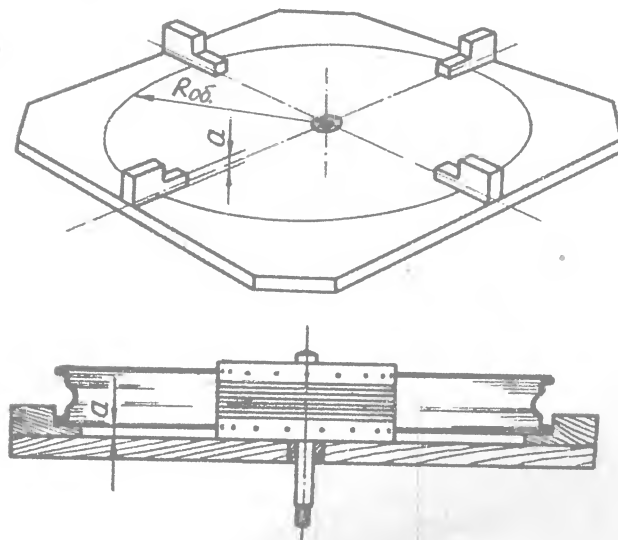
Приспособление для сборки колеса: а — величина выступа барабана за плоскость обода.
